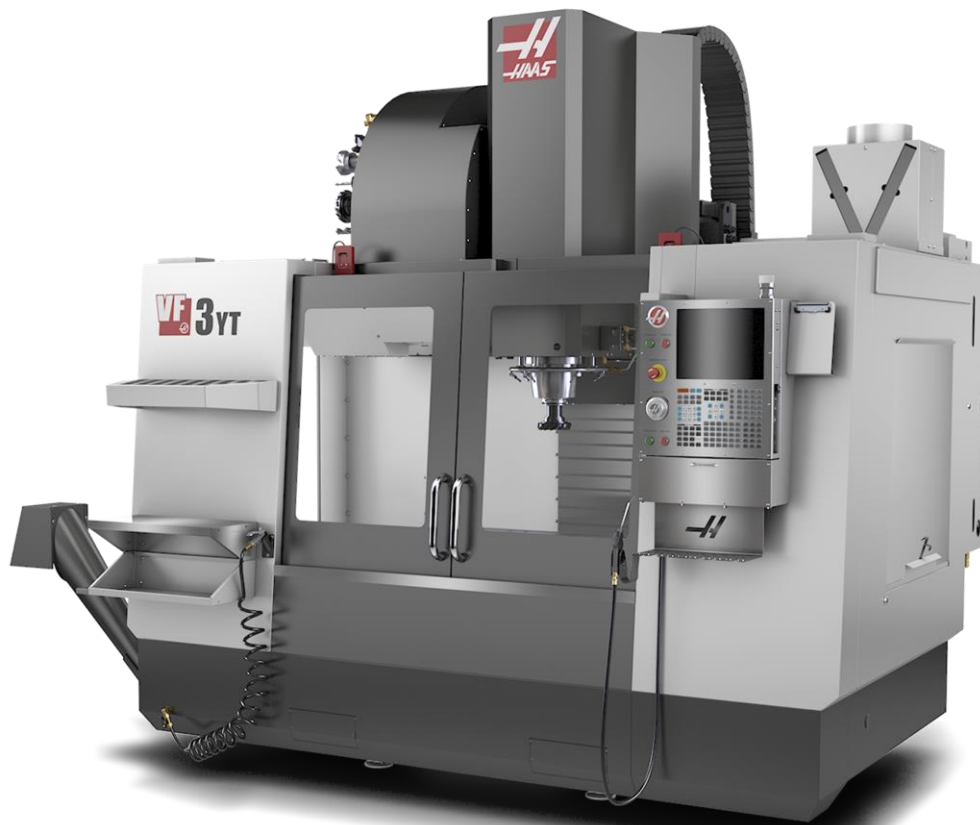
Вертикально-фрезерний верстат з ЧПК Haas VF-3YT/50
